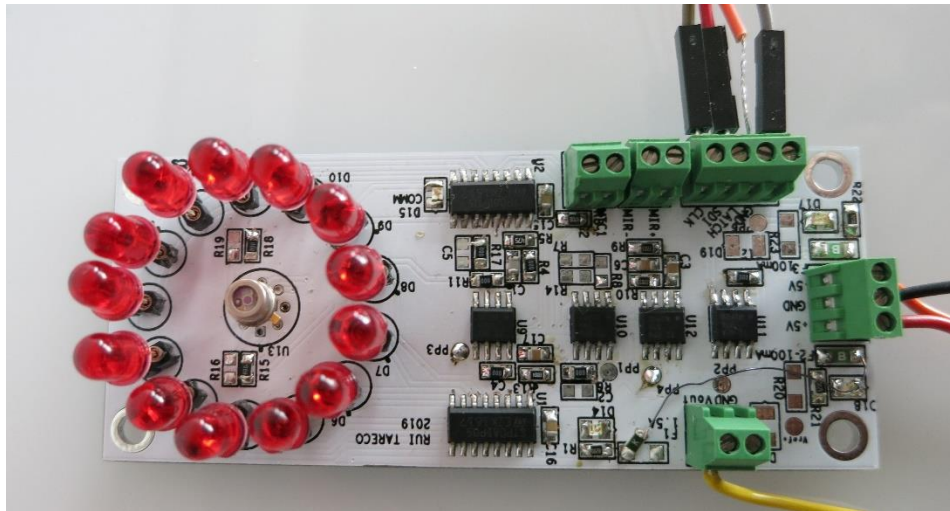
PCB já soldada para a 1ª abordagem com LED de Teste
